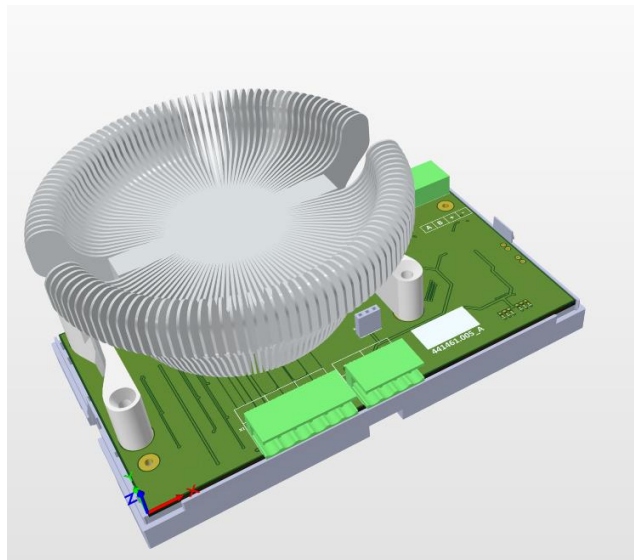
3D модель корпуса B6505113 с кулером
